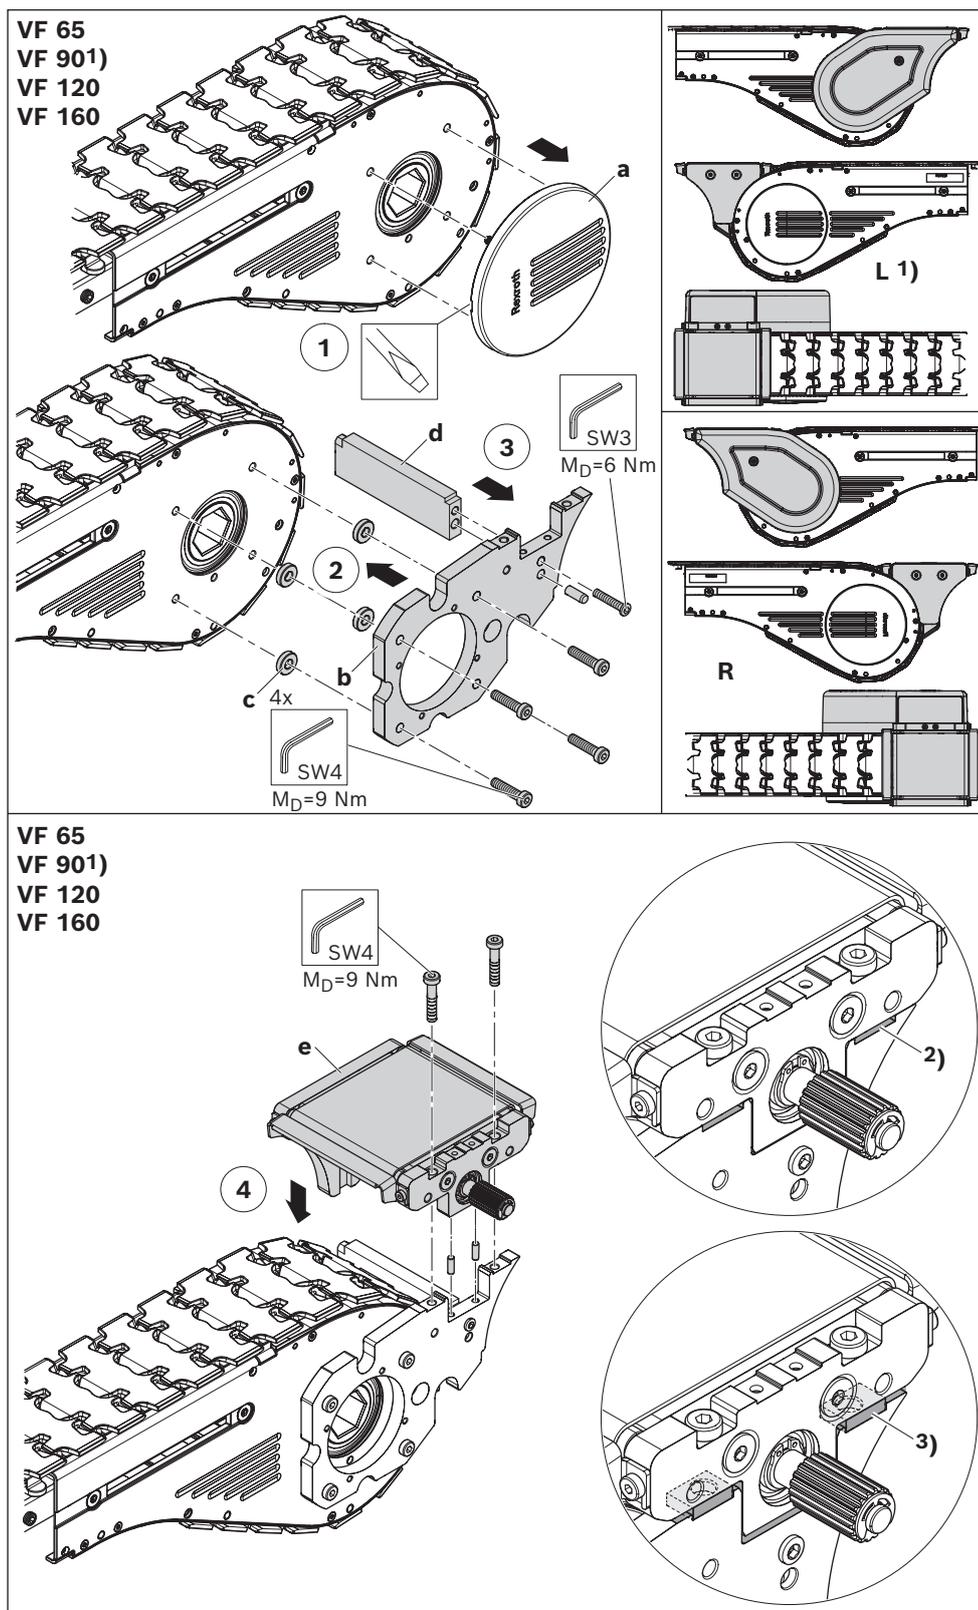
Set di collegamento attivo, montaggio del tappeto (ponte a tappeto) (1/4)
